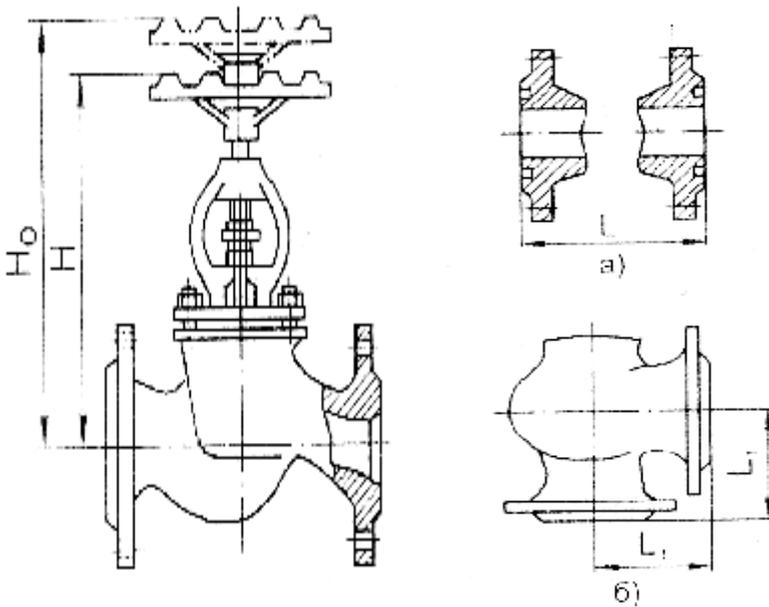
Строительная высота арматуры:  $H$  – в закрытом виде;
